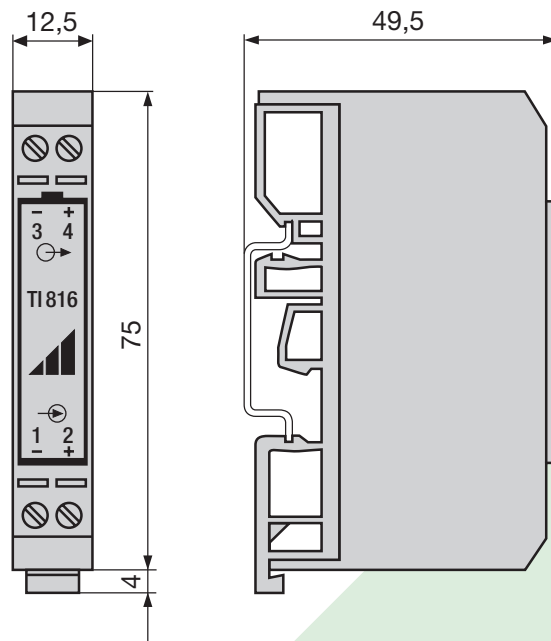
SINEAX TI 816 en boîtier pour montage sur rail N12 sur barre à profil en chapeau EN 50 022 – 35x7,5.
